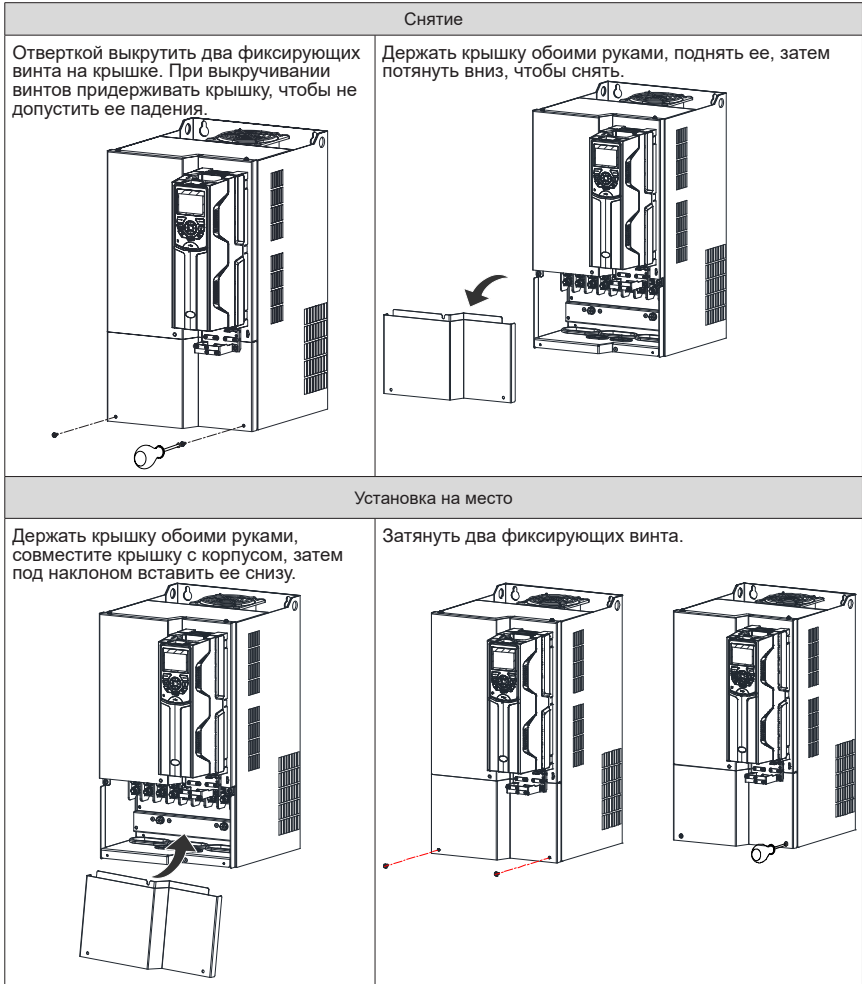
Снятие и установка крышки конструкций Т2 - Т9
